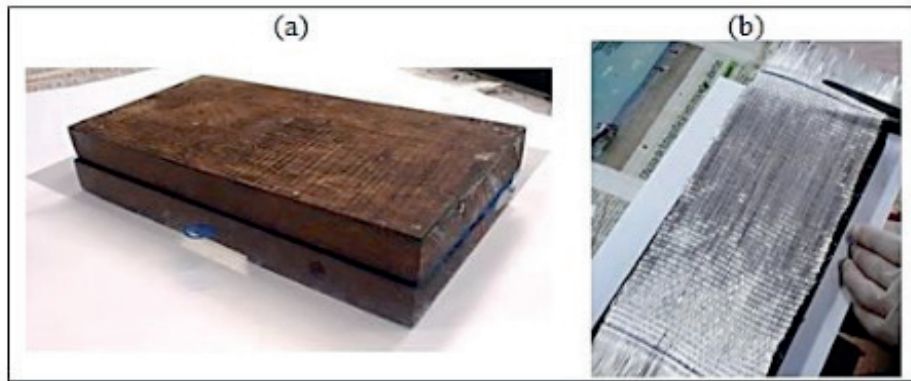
(a) Molde superior e inferior de madeira (b) Corte da lâmina de vidro nas dimensões do molde.
